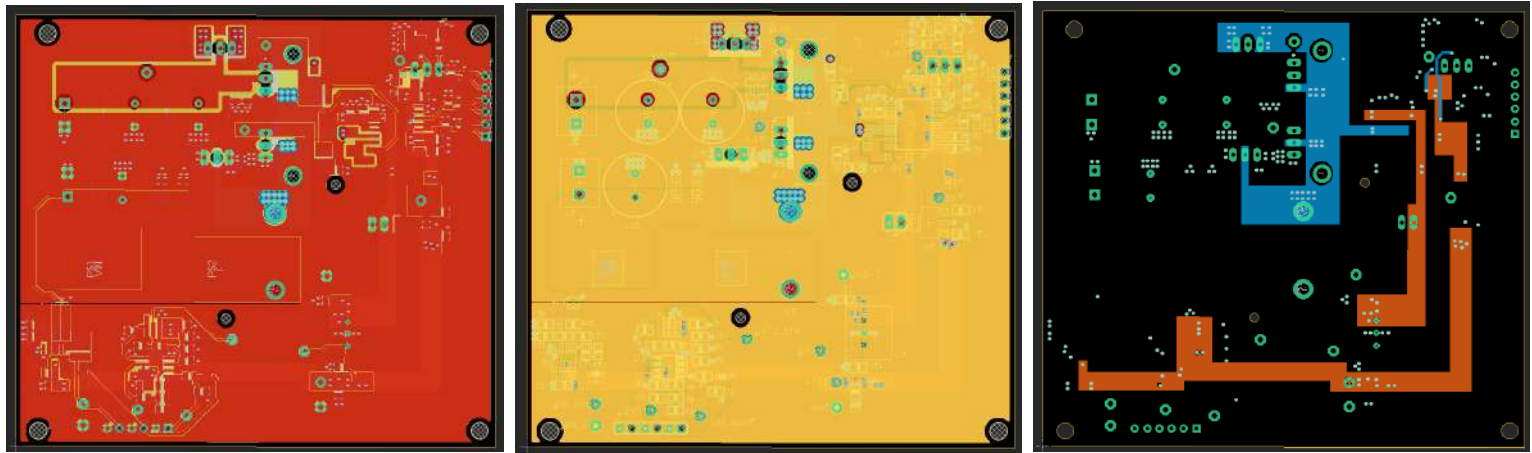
layout PCB - capa superior (señal) - capa 2 (GND) - capa 3 (PWR) e inferior (señal).
